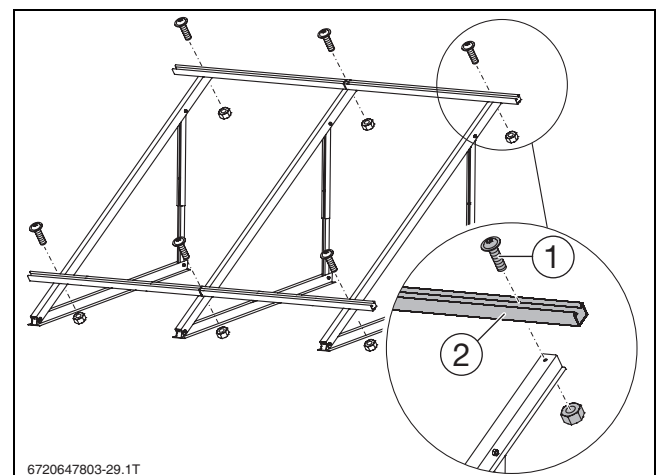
Montagem das calhas de perfil (aqui: 2 colectores verticais)
